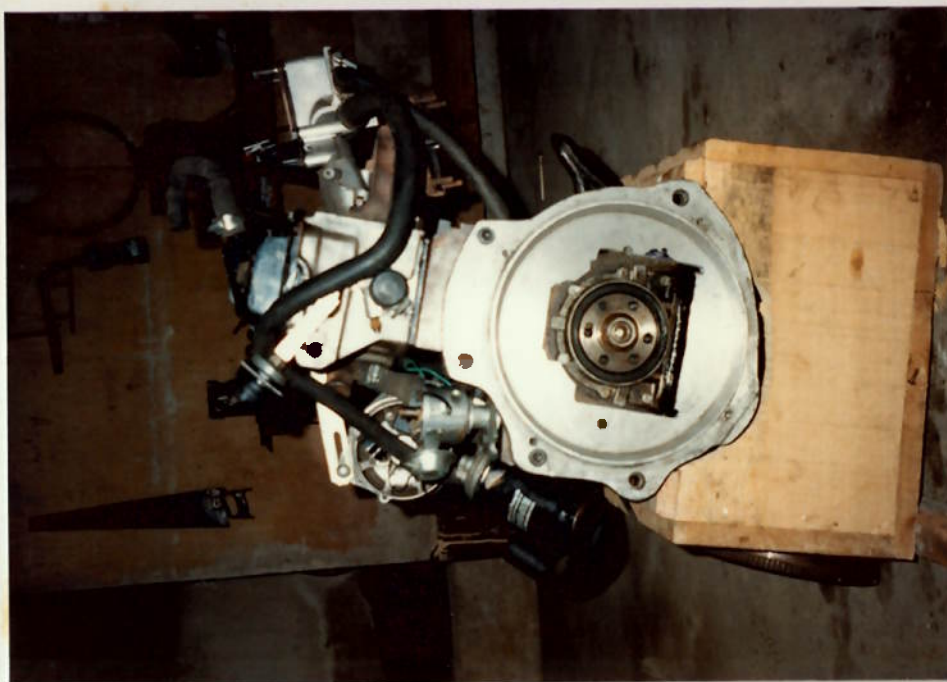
Vista frontal do motor mostrando o flange de adaptação à caixa de câmbio. Observar detalhe de fixação do volante do motor ao virabrequim.
